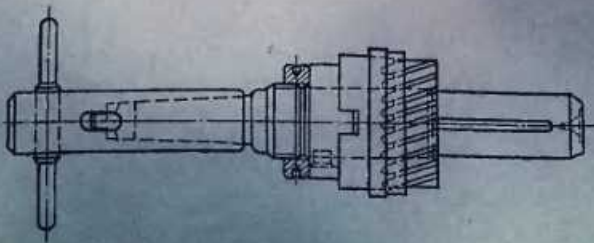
Коническая развертка для снятия фасок на вкладыше шатуна
